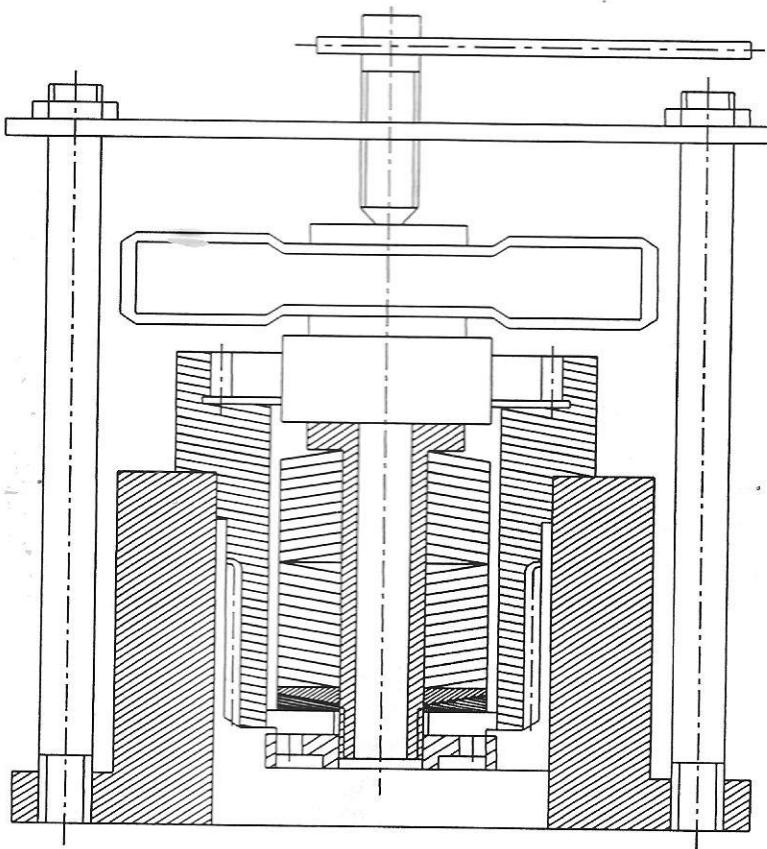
Сборочный узел для предварительного нагружения пакета тарельчатых пружин
